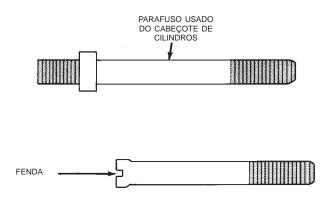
Conjunto do Cabeçote de Cilindros do Motor INSTALAÇÃO
